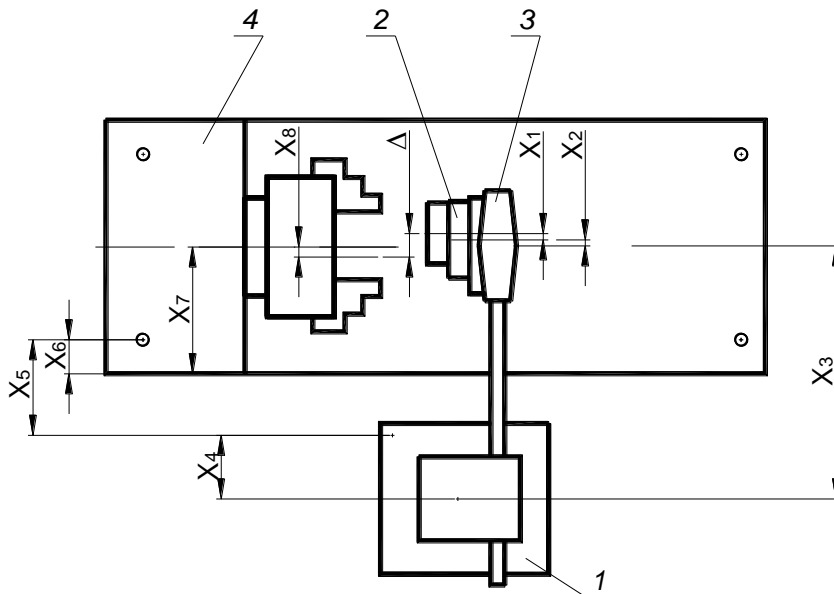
Размерная цепь при установке детали в патрон токарного станка
